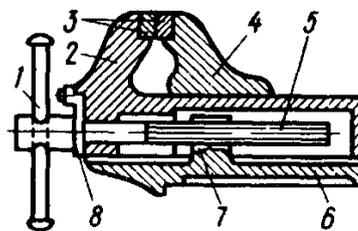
Слесарные неповоротные тиски с ручным приводом
